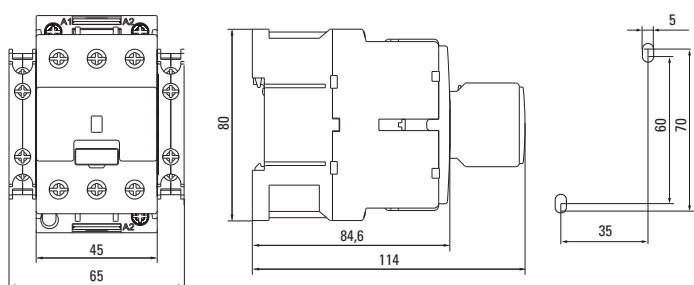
Габаритные и установочные размеры контакторов KM3 32A, KM3 38A
